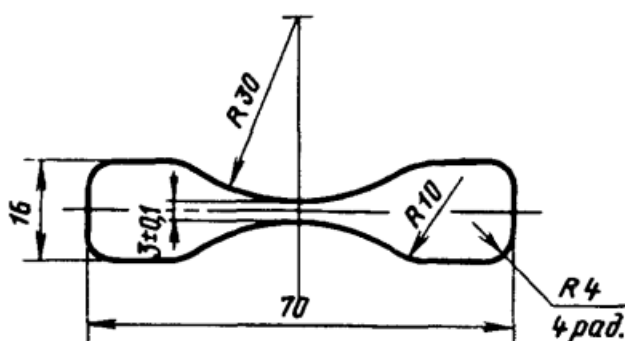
Схема стандартного зразка гумового виробу для випробовування на фізико-механічні властивості.
